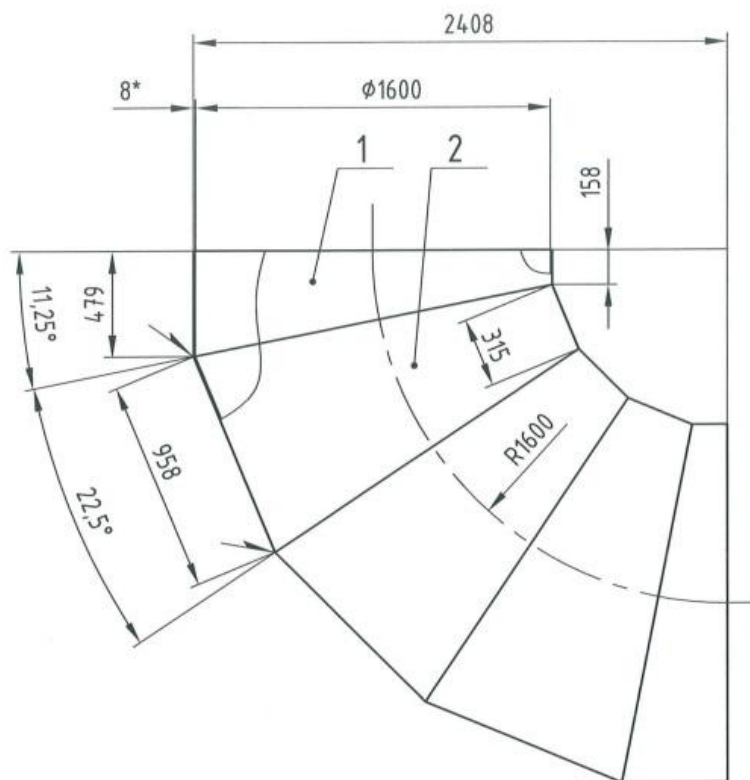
Отвод сварной 90-DN 1600
